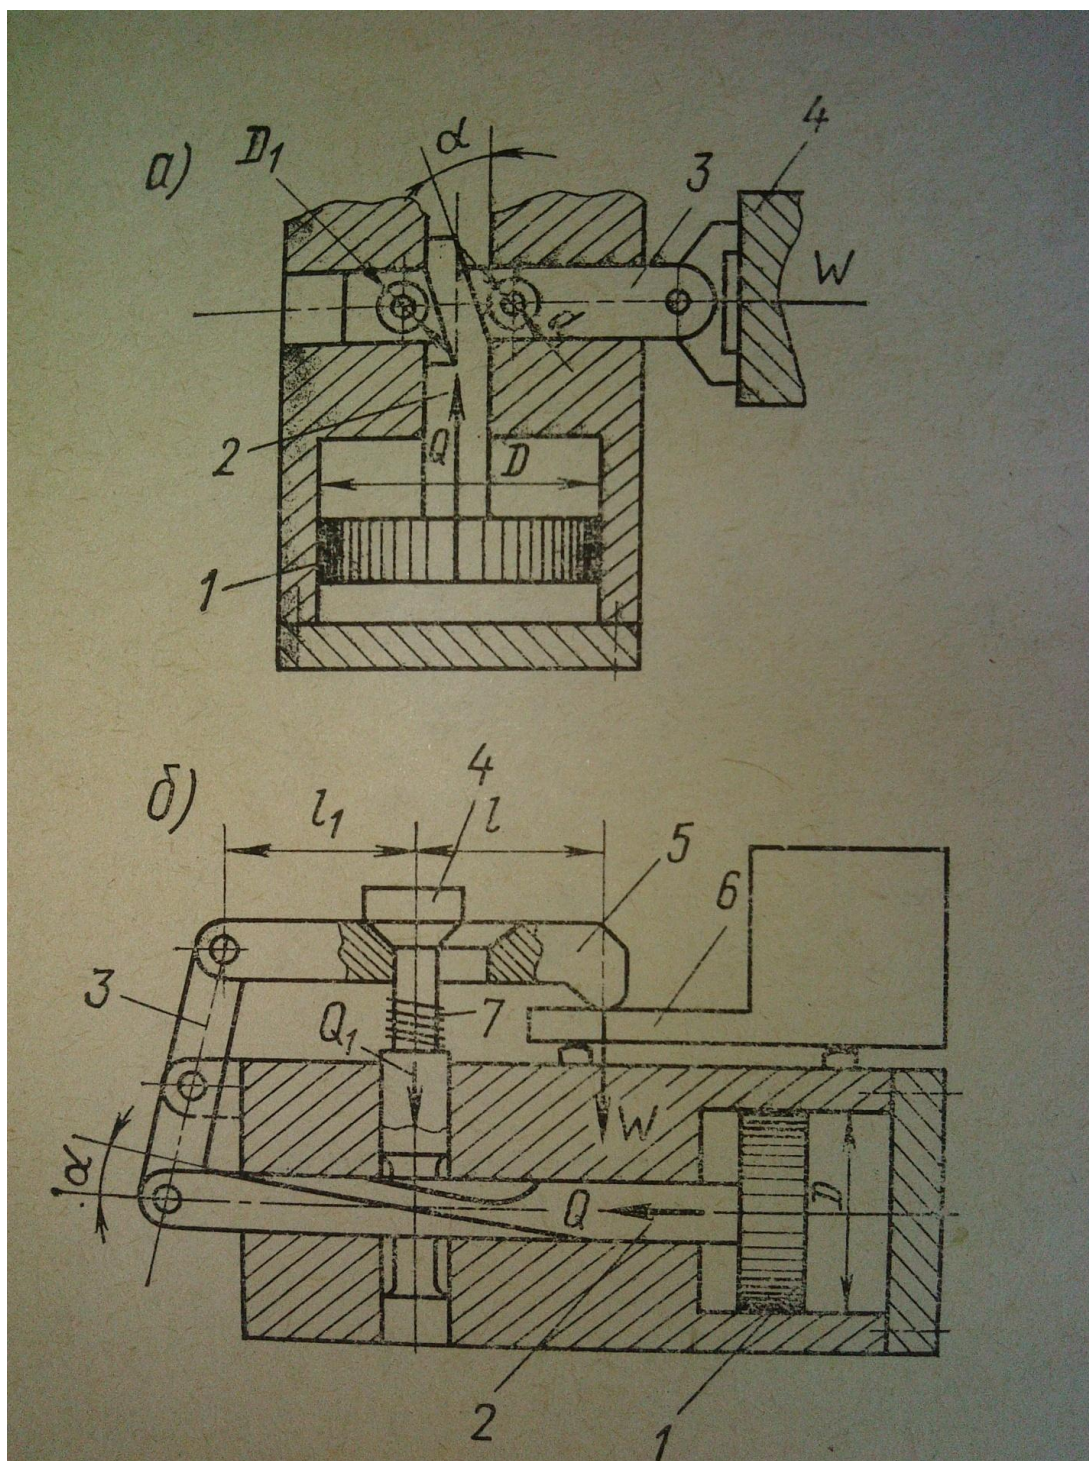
Схема клиноплунжерного усиливающего затискного пристрою
